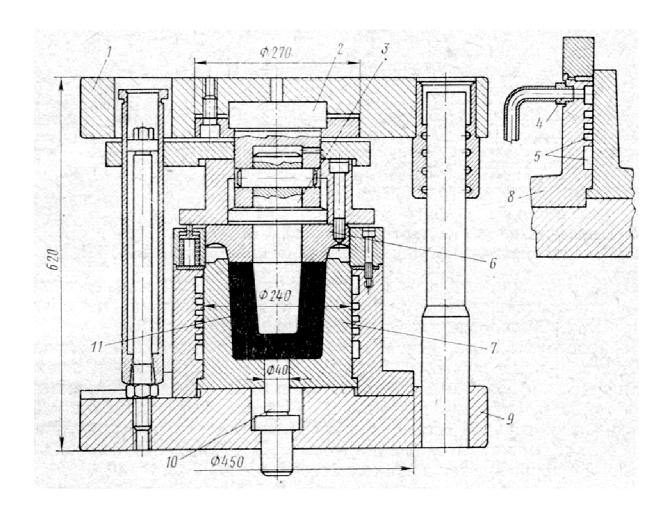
Схема штампа для жидкой штамповки полой поковки: 1 — верхняя плита; 2 — блок пуансонов; 3 — прошивной пуансон; 4 — водяной шланг; 5 — каналы для водяного охлаждения; 6 — подпрессовый пуансон; 7 — матрица; 8 — обойма матрицы; 9 — нижняя плита; 10 — выталкиватель; 11 — поковка
